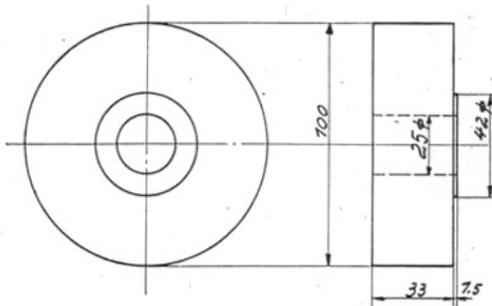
Maßskizze des Auflagestückes für die Kurbelgehäusehälften beim Eindrücken der Rollenlaufringe
